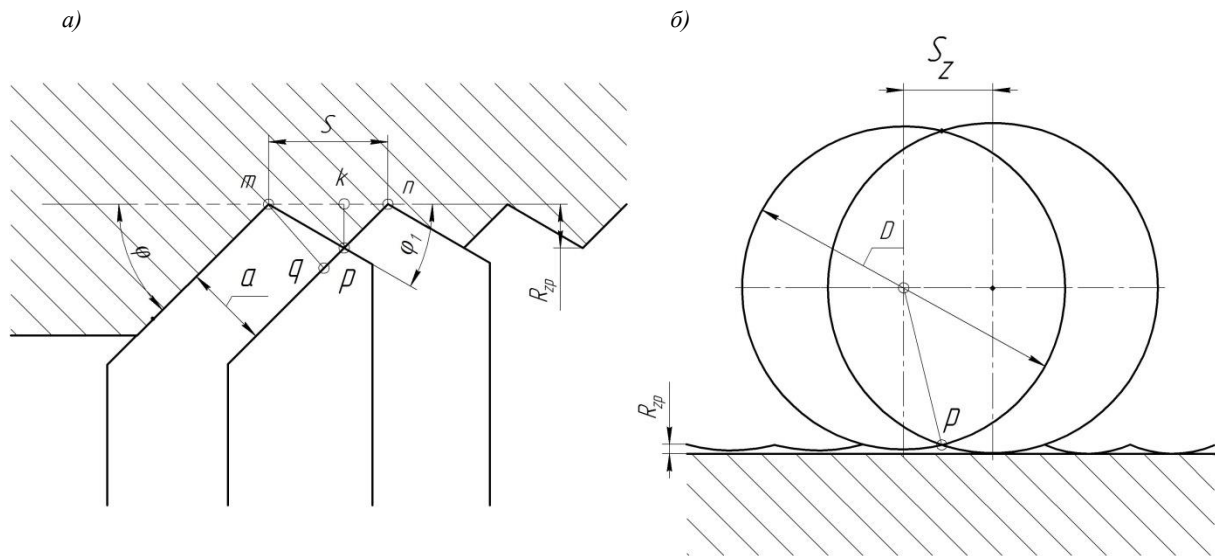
Теоретичний мікропрофіль оброблюваної поверхні при точінні (а) і фрезеруванні циліндричними фрезами (б)
